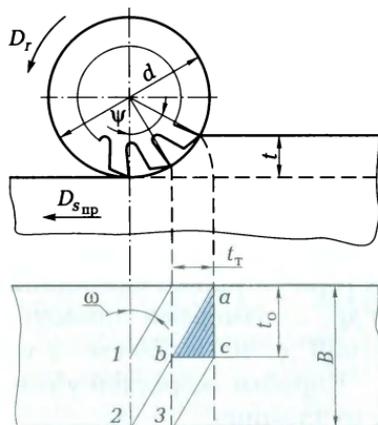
Схема расположения зубьев при равномерном фрезеровании:
